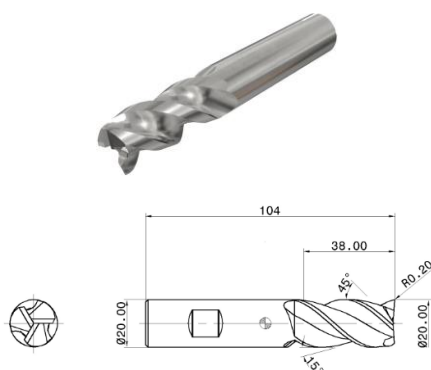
Кінцева фреза ECA-B-3 20-38W20-104
